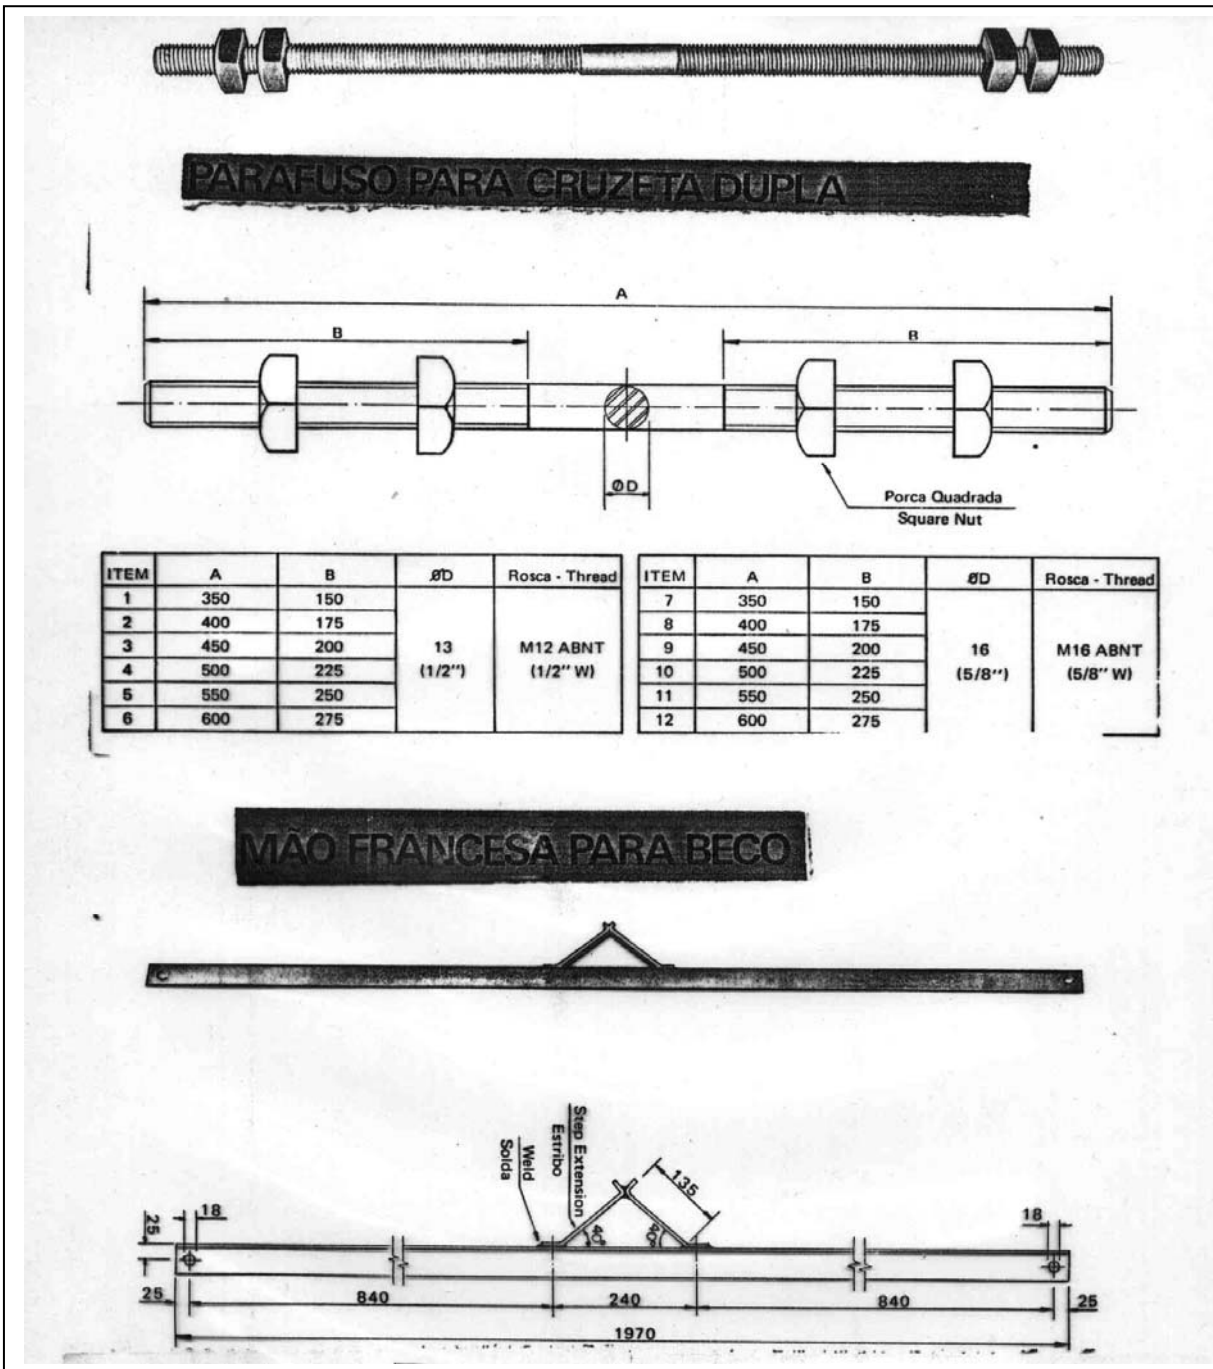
Dimensões de Parafuso de Cruzeta Dupla e Mão Francesa para Beco
